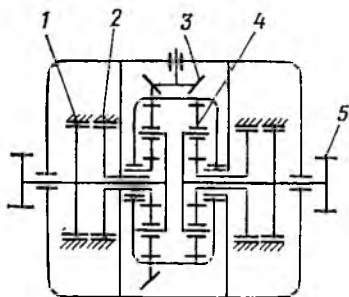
Кинематическая схема заднего моста с планетарными механизмами поворота:
